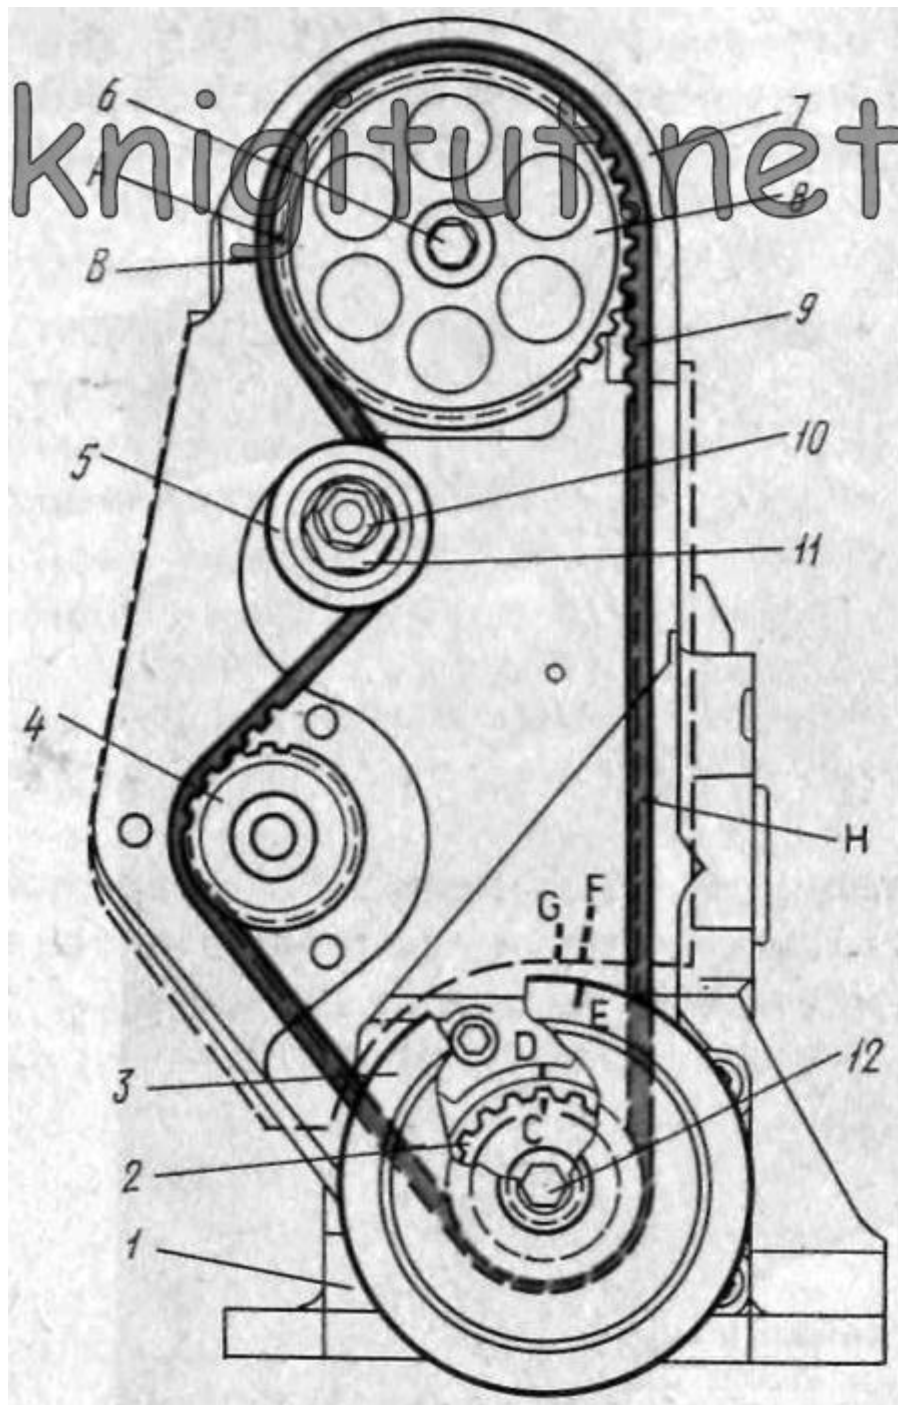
Схема привода механизма газораспределения автомобиля ВАЗ-2108: 1 — корпус масляного насоса, 2 — зубчатый шкив коленчатого вала, 3 — шкив коленчатого вала, 4 — валик привода водяного насоса, 5 — ролик натяжного устройства, 6 — болт, 7 — передняя защитная крышка, 8 — шкив распределительного вала, 9 — зубчатый ремень, 10 — гайка эксцентрика, 11 — эксцентрик, 12 — болт; А — метка на шкиве распределительного вала, В — указатель на задней защитной крышке, С — метка на зубчатом шкиве коленчатого вала, D — метка на кор-
